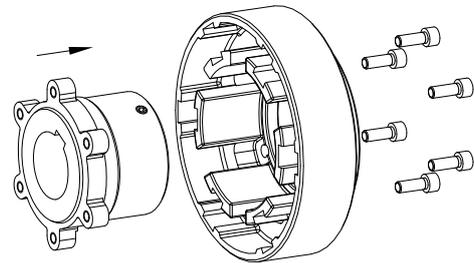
montaggio della flangia del mozzo con l'anello a settori frontali
